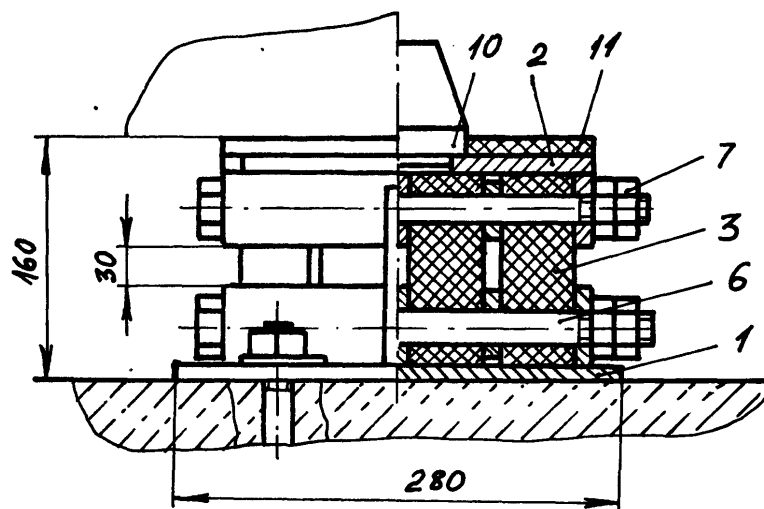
Пружна опора ОУ-4: 1 - нижня основа; 2 - верхня основа; 3 - пружний гумовий елемент; 4 - подовжньо ребро нижньої основи; 5 - поперечне ребро; 6 - болт; 7 гайка; 8 - фундаментний болт; 9 - рухлива рама віброплощини; 10 - посадковий виступ; 11 - демпфіруюча прокладка; 12 - строповочний отвір
